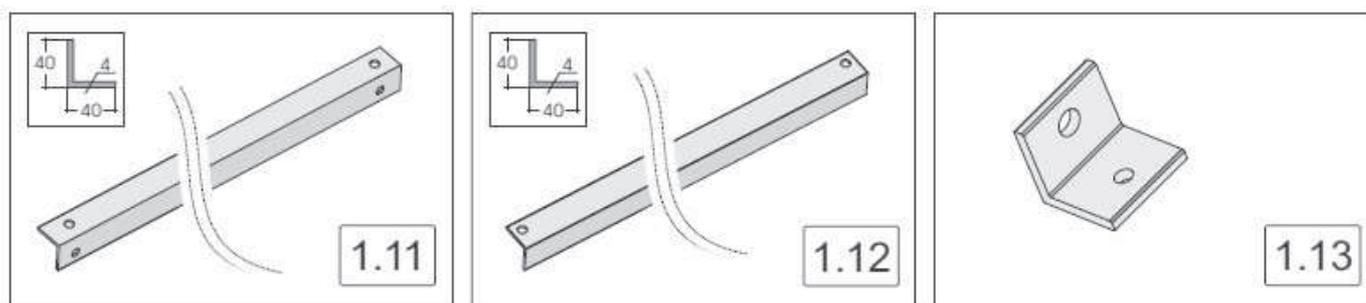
Montage sur châssis à 45° – Principaux composants.
